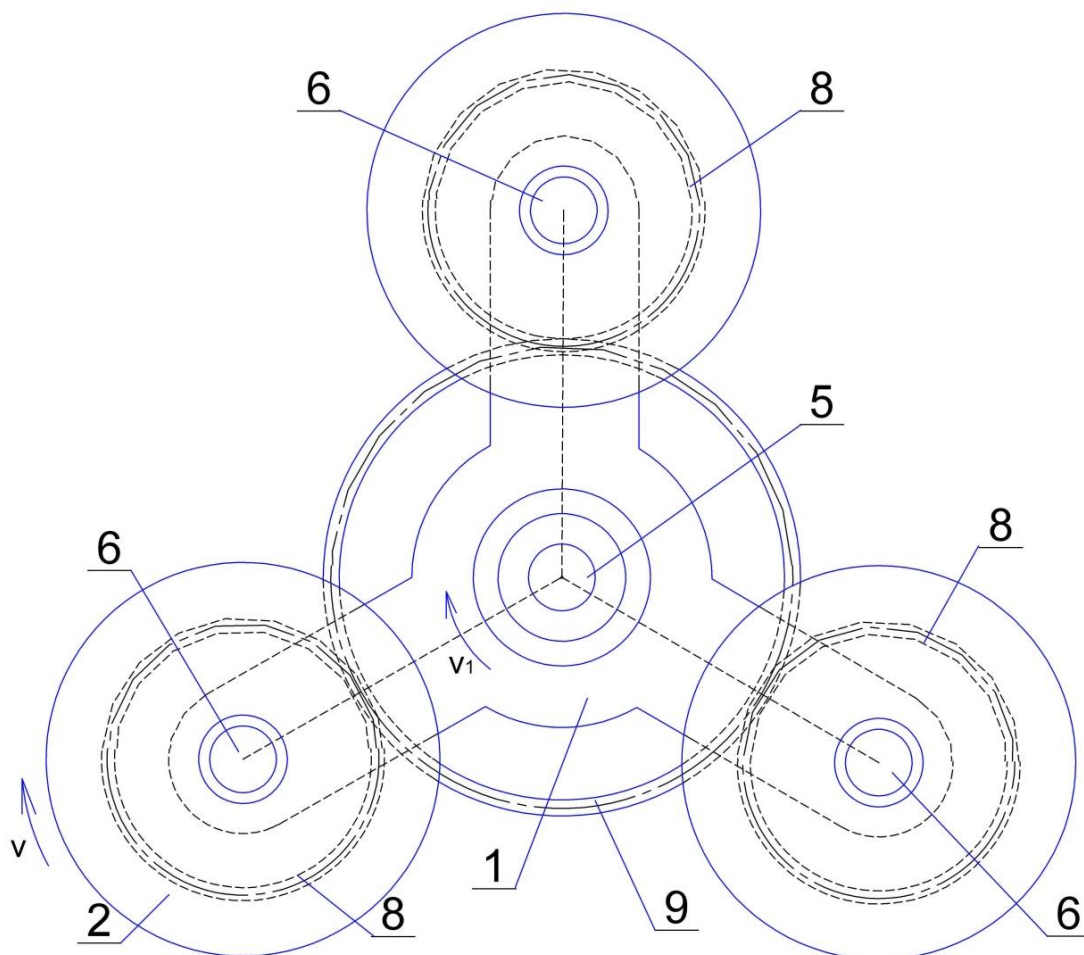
Загальний вигляд водила з встановленими додатковими шпинделями та торцевими фрезами
